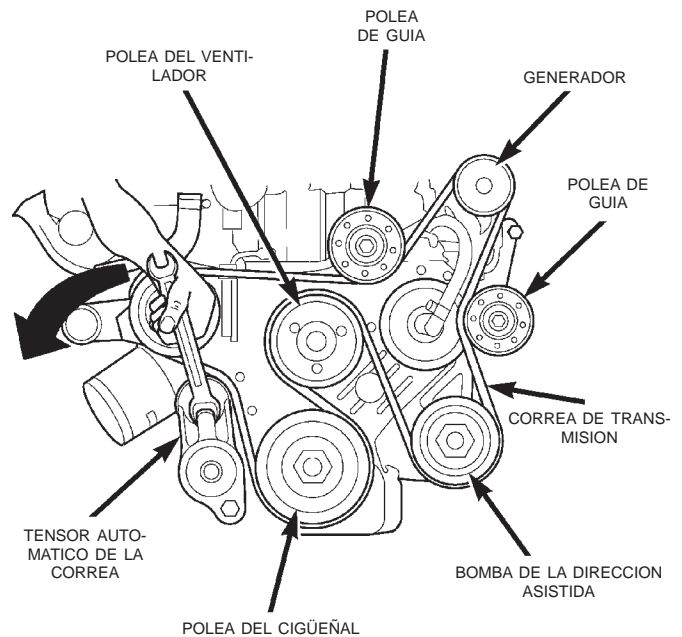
Conjunto de tensor automático de la correa BOMBA DE AGUA
